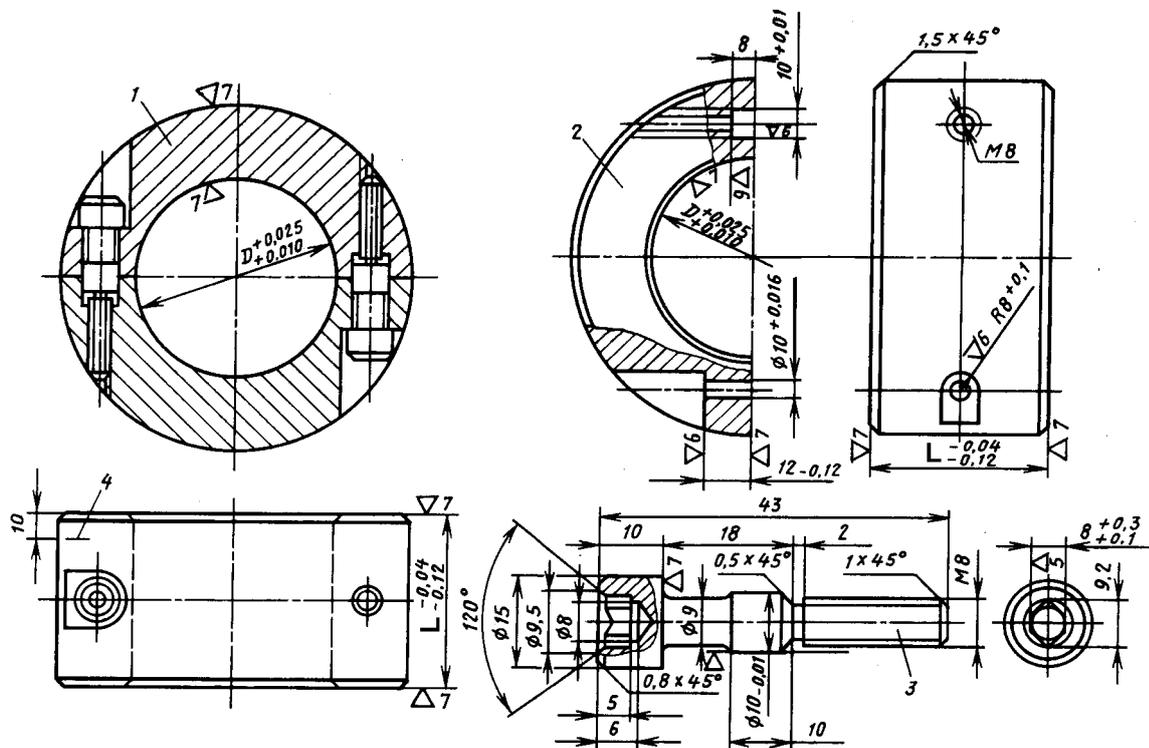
Балансировочный груз, устанавливаемый на шатунные шейки коленчатого вала:
